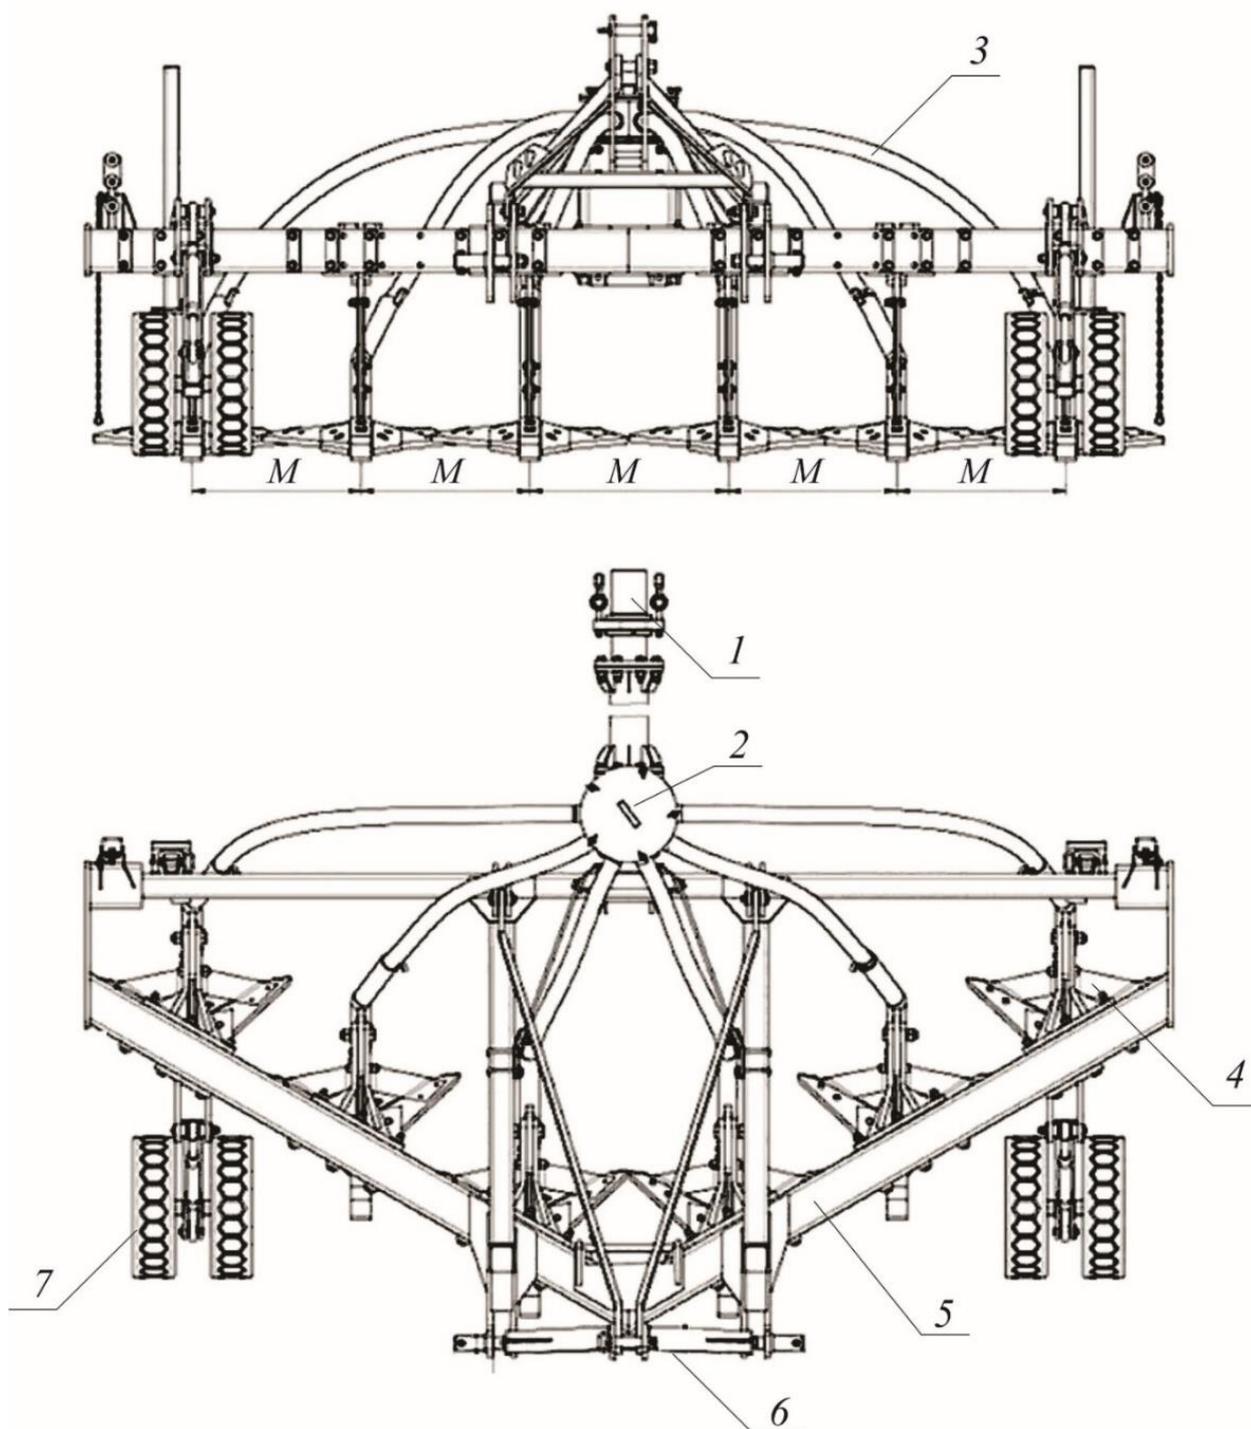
Общий вид чизельного глубокорыхлителя для
